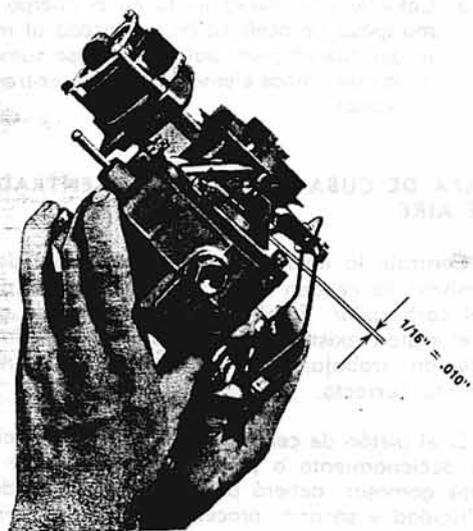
Tolerancia de la ventilación de la cuba del carburador.
